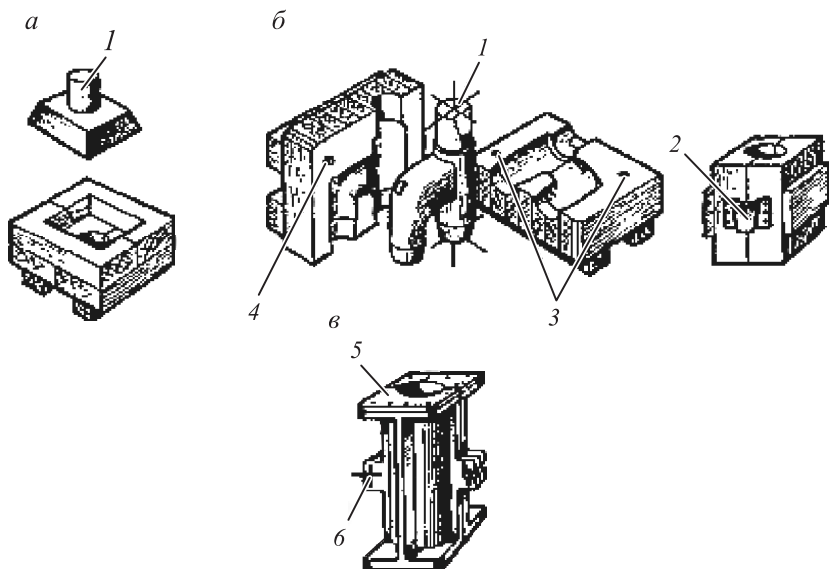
Стержневые ящики для ручной формовки стержней:
